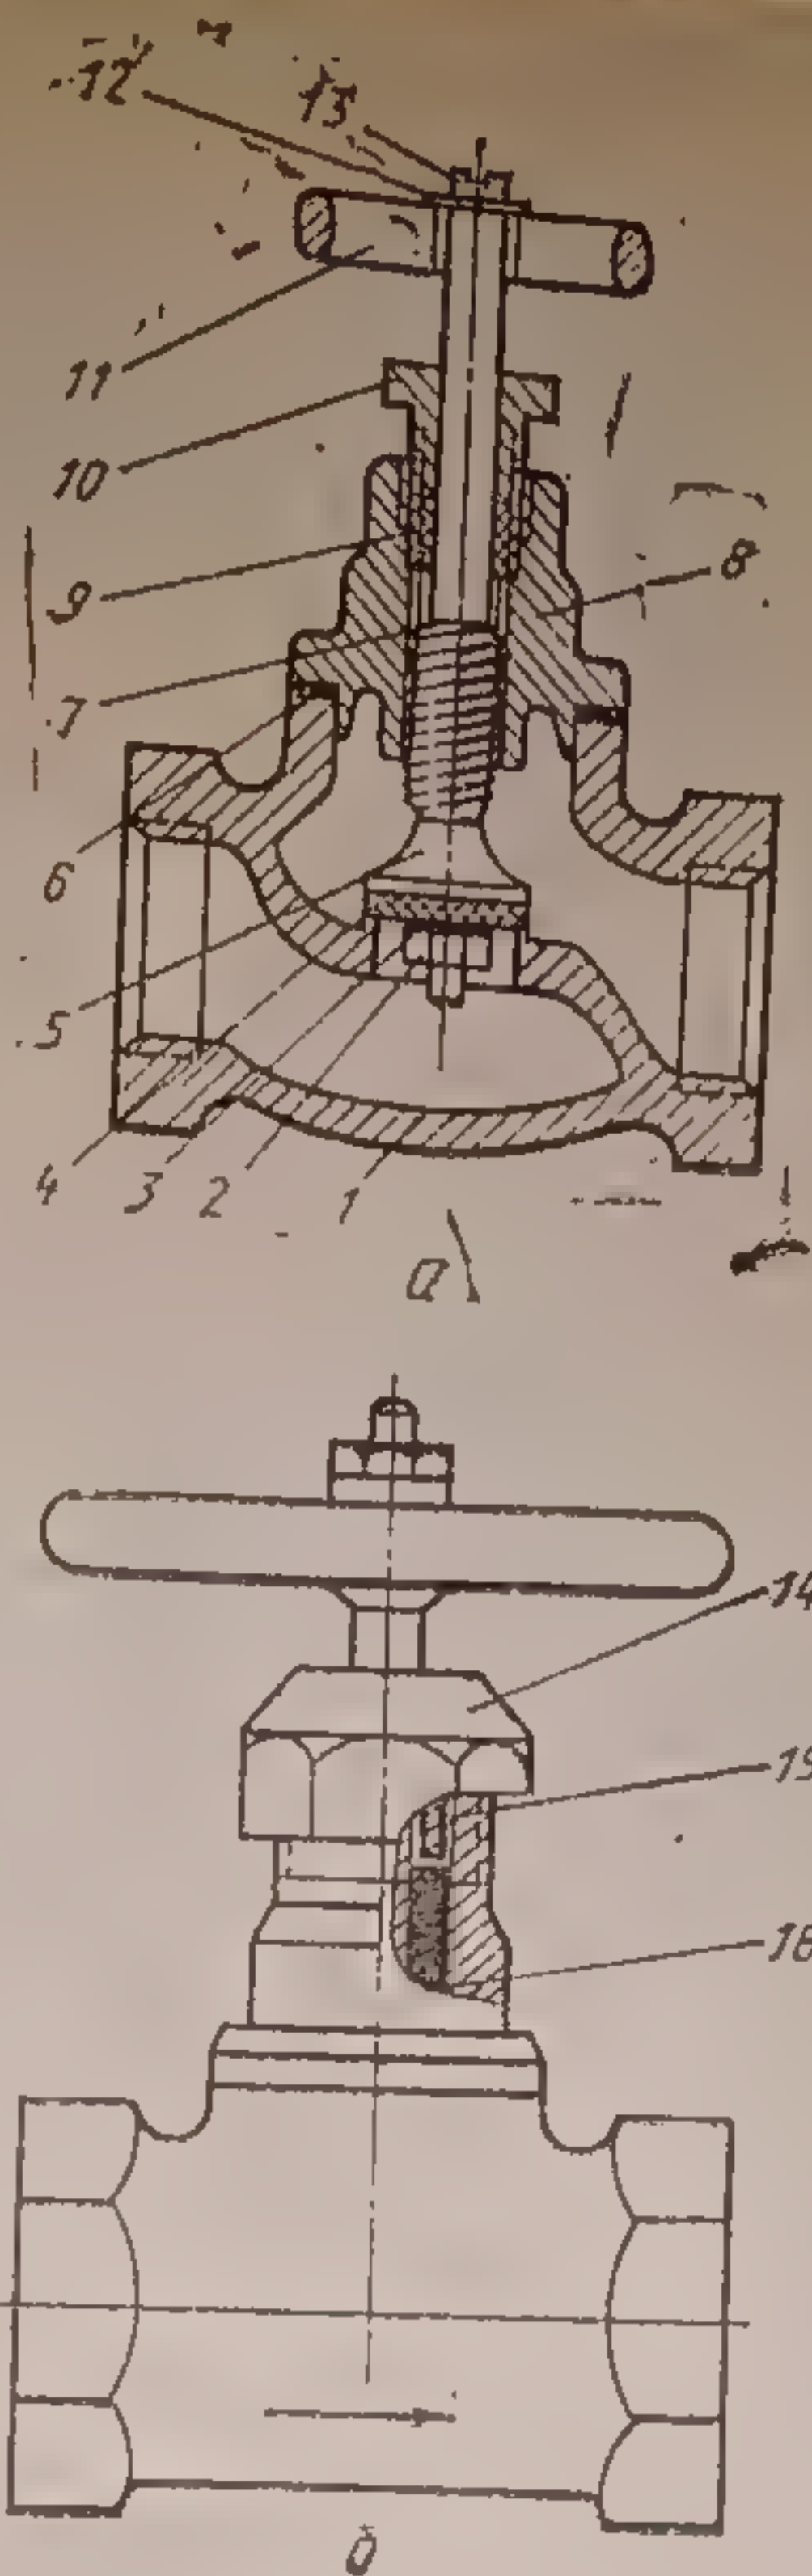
Вентили: а — со спецштулкой; б — с накидной гайкой; 1 — корпус; 2 — гайка; 3 — шайба; 4 — прокладка резиновая; 5 — клапан; 6 — прокладка из льна или паранита; 7 — шток; 8 — головка корпуса; 9 — сальниковая набивка; 10 — спецштулка; 11 — маховик; 12 — шайба; 13 — винт; 14 — накидная гайка; 15 — втулка сальника; 16 — сальник
